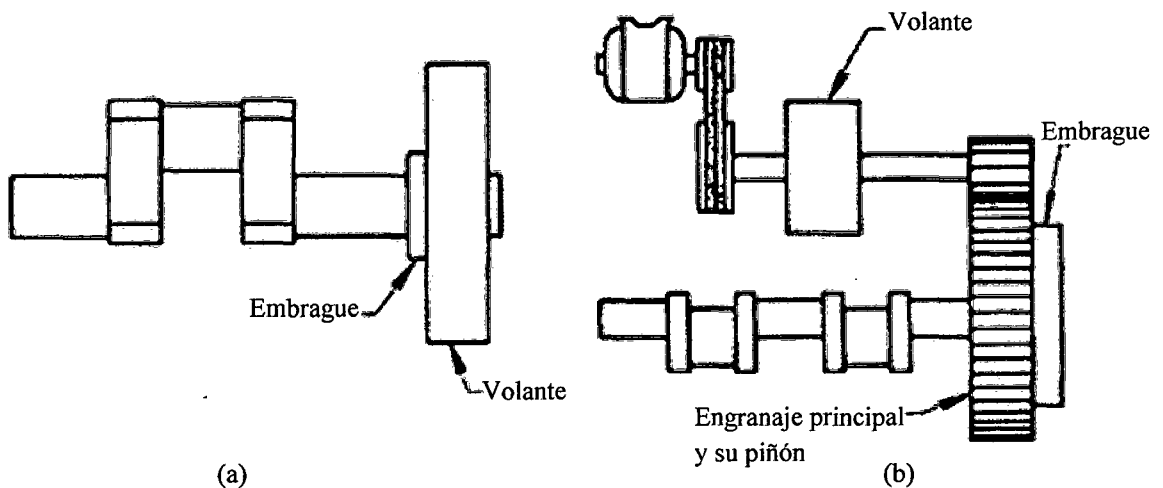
Tipos de Transmisión Mecánica: a) No Engranado b) Engranado.
